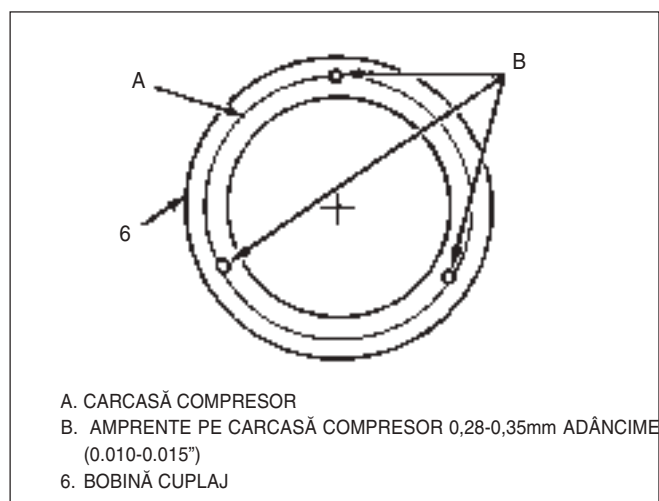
Detaliu cap amprentat pt fixare bobină cuplaj
